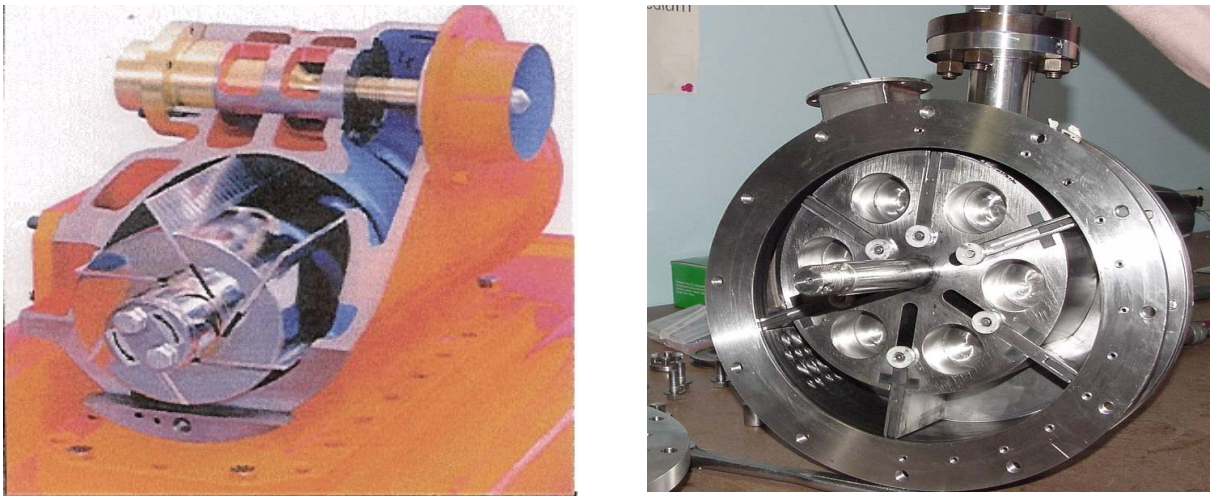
Compresor (izquierda) y turbina rotatoria (derecha) de desplazamiento positivo
